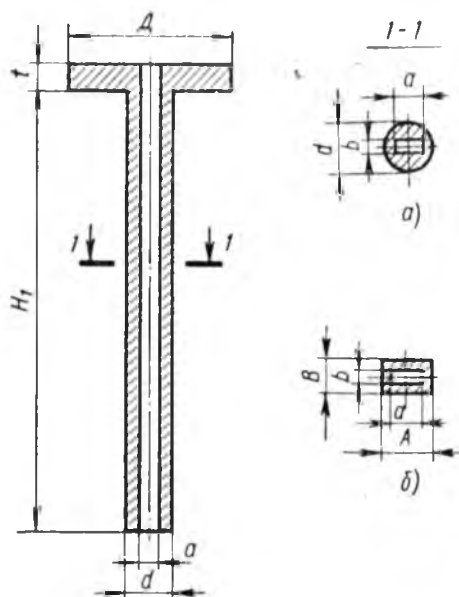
Деталь волноводного корпуса, изготовленная методом холодного выдавливания
